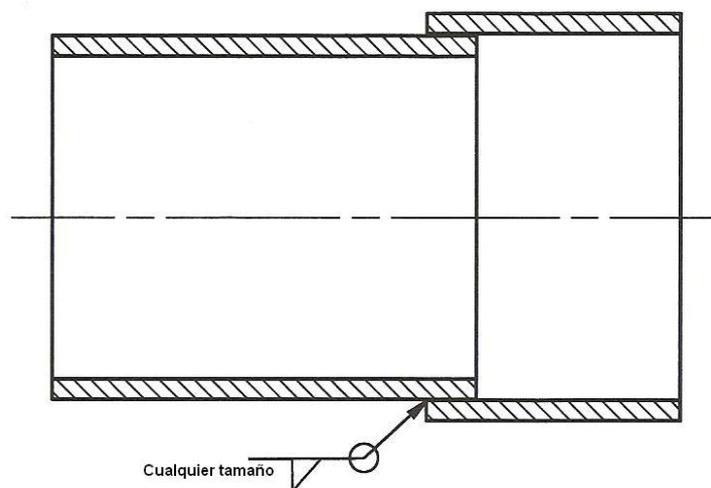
Probeta para Calificación de Soldador de Filete o para Punteador, Caño o Tubo
